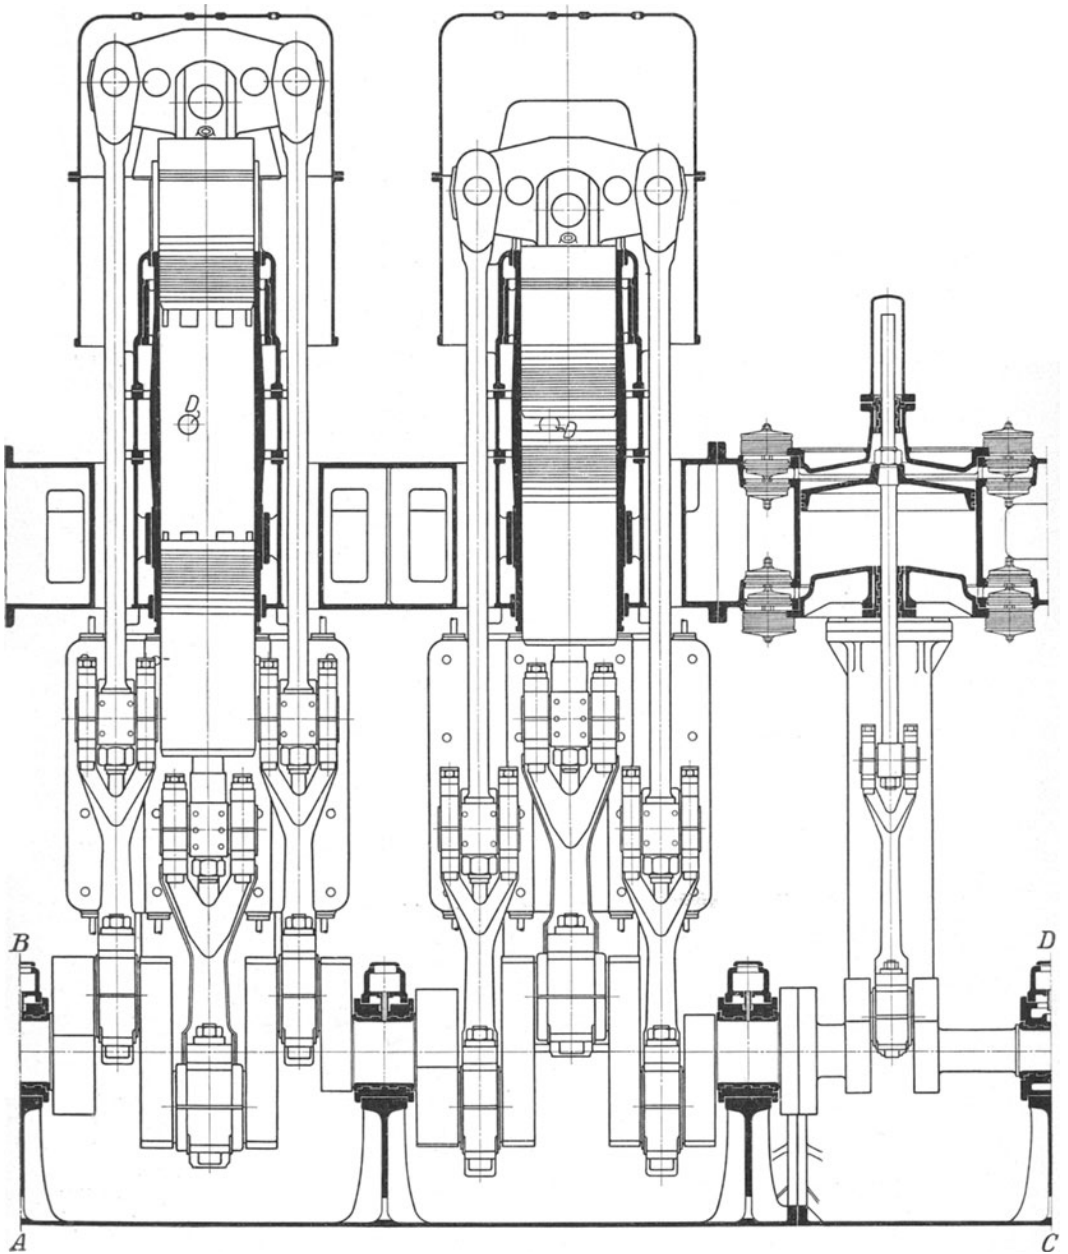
Schnitt durch Arbeitszylinder und Spülpumpe einer Junkers-Ölmaschine.
